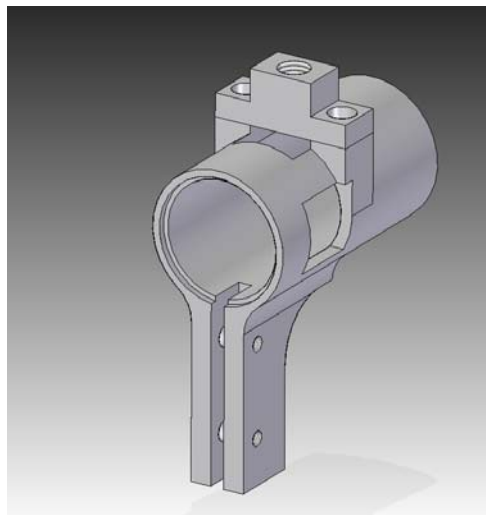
Detalle del Puente Fijación (B-009) sobre .
